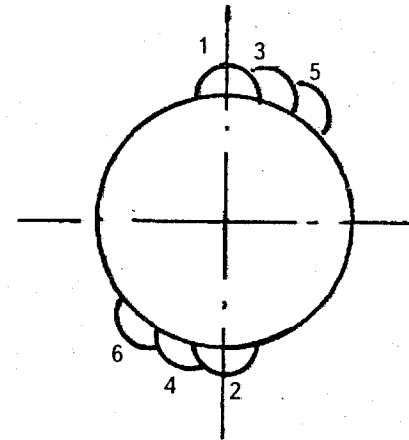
Порядок наложения швов при наплавке деталей цилиндрической формы продольными валиками
